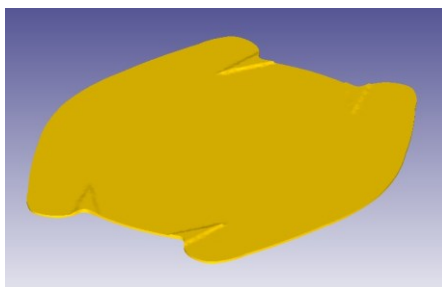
Заготовка с утолщением в местах предполагаемого разрыва.
